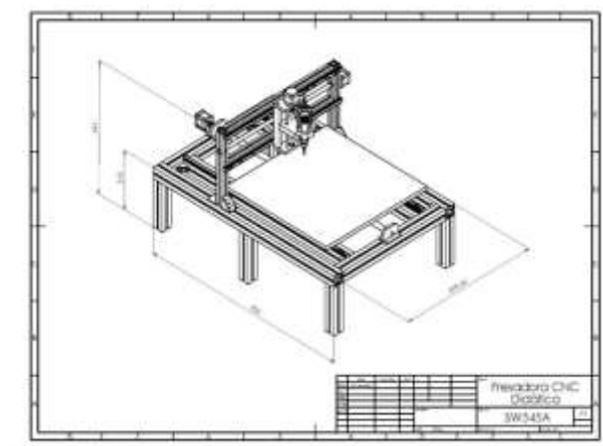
Croqui da Fresadora CNC de Bancada Didática
